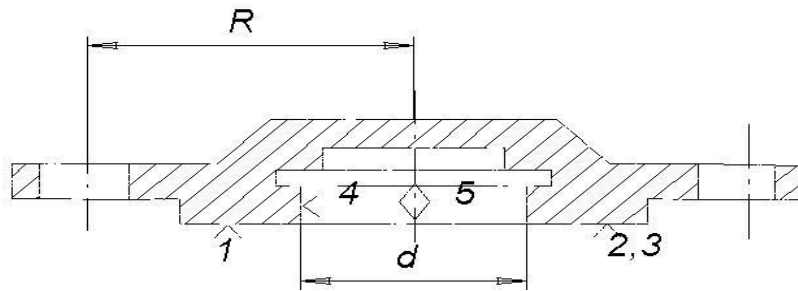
Базування по торцю і внутрішній циліндричній поверхні.
